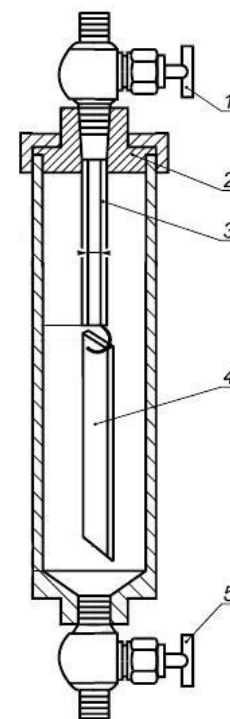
Цилиндр высокого давления ЦВД: 1 – игольчатый клапан А; 2 – фторсиликоновое уплотнительное кольцо; 3 – выпускная трубка; 4 – медная пластинка; 5 - игольчатый клапан В.
